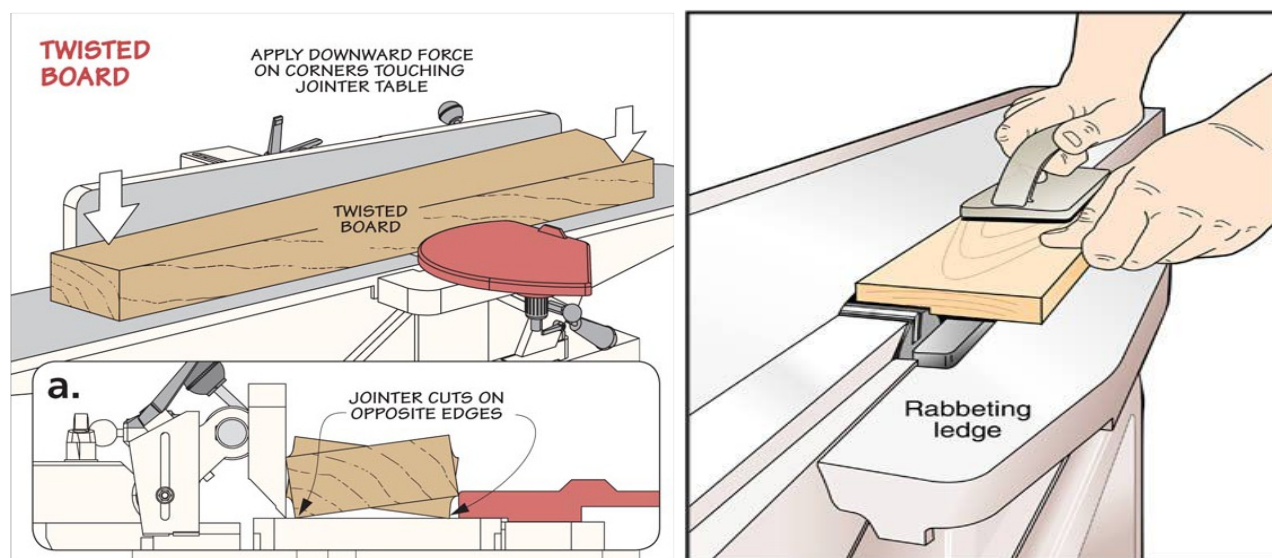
Обробка заготовок з крилатістю та виборка чвертей
